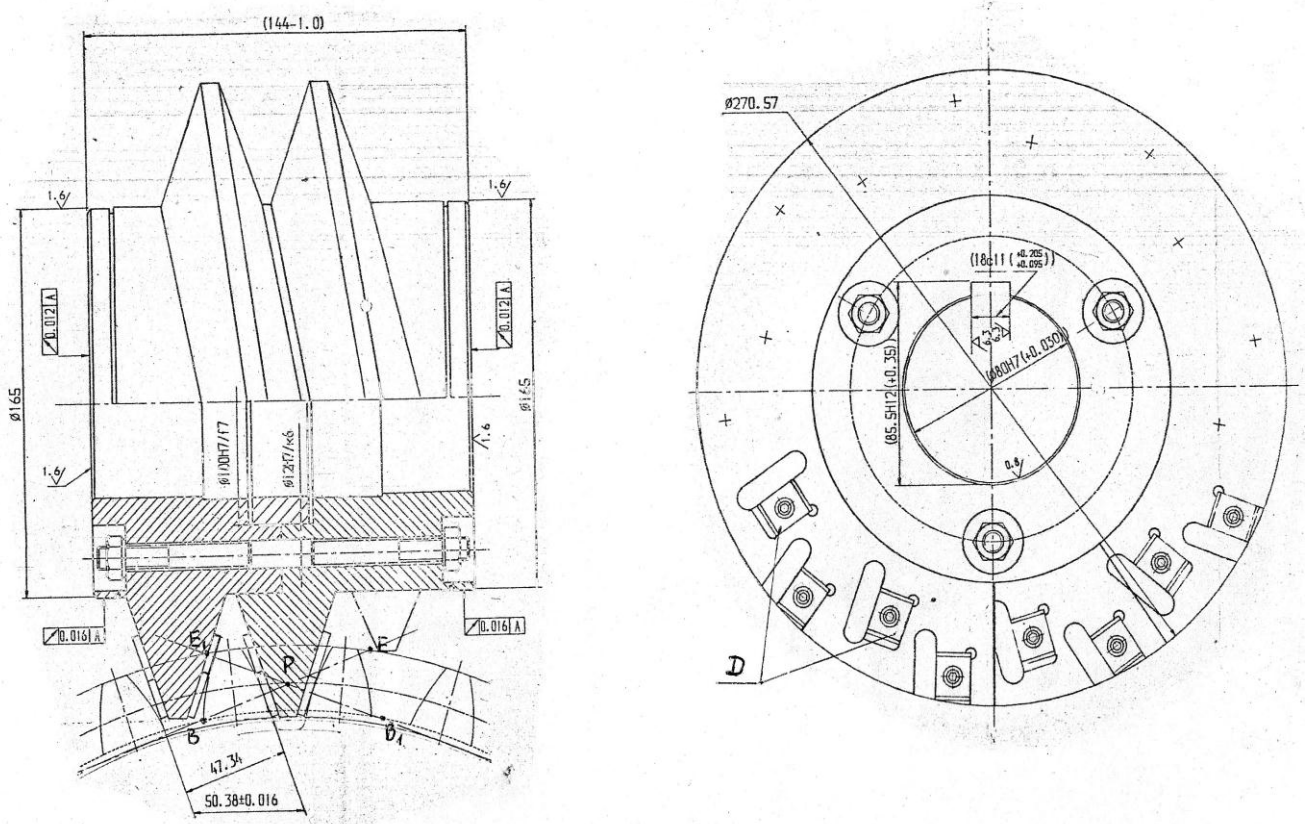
Однокорпусная двухсторонняя фреза $m=20$ мм с дополнительными пластинками
